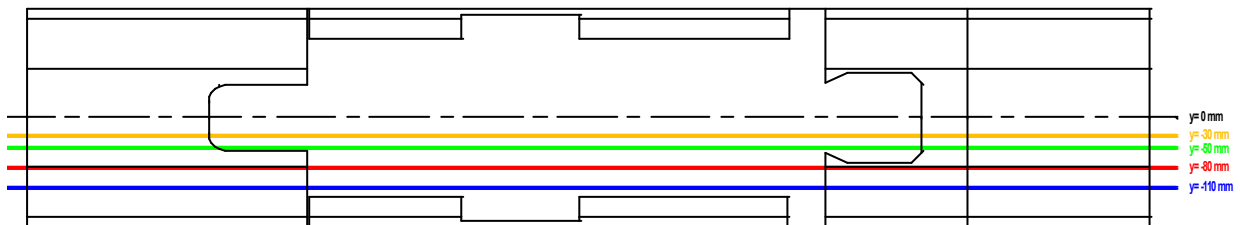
Cotes y des différents plans transversaux de la première campagne.
